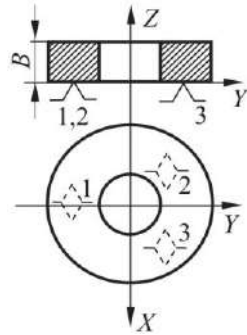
Установка заготовки з позбавленням трьох ступенів свободи
